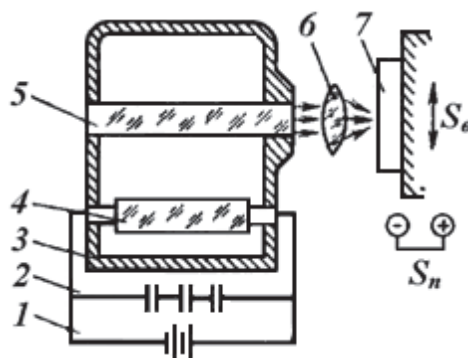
Схема оптичного квантового генератора: 1 – джерело струму; 2 – батарея конденсаторів; 3 – корпус; 4 – імпульсна лампа; 5 – рубін; 6 – лінзи; 7 – заготовка
